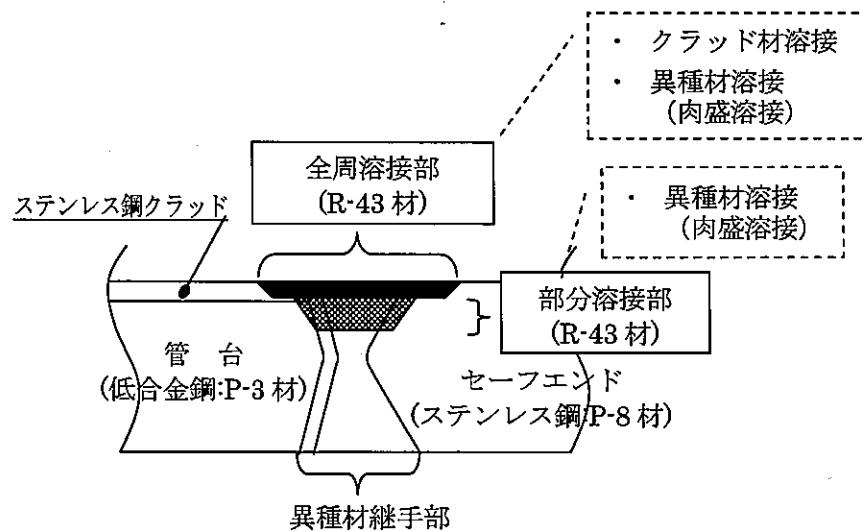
テンパーべード溶接 施工対象 (例 : 原子炉容器)
